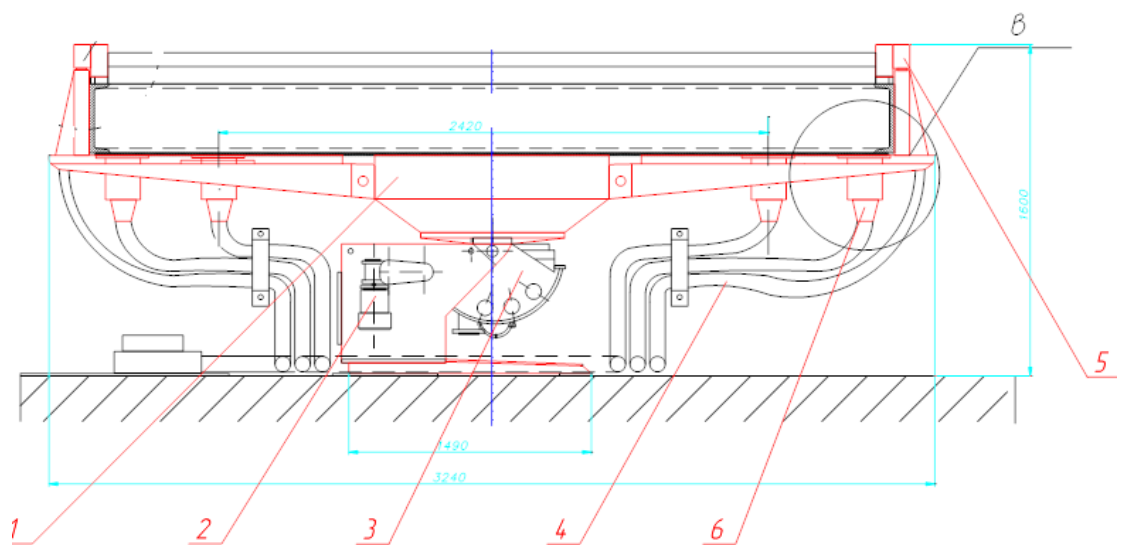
Стенд для складання каркасу рами з обшивкою
